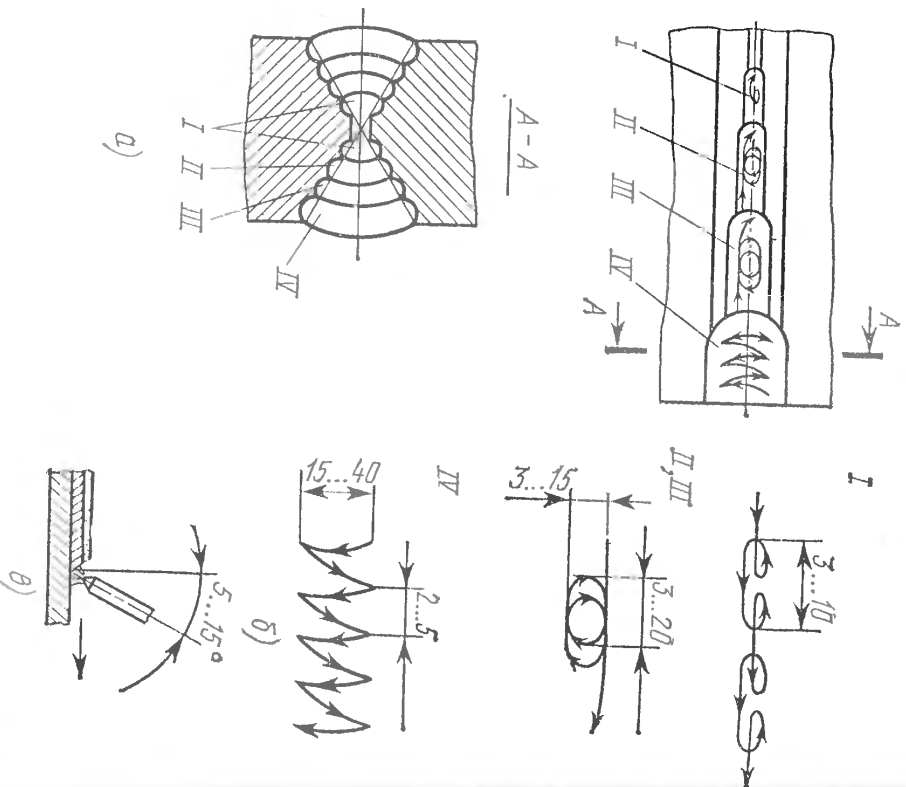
Траектория движения и размеры колебаний горелки при наложении многослойных стыковых швов в пространстве сварки в углекислом газе:
